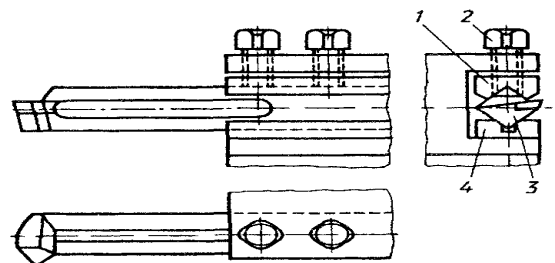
Жорсткий розточувальний різець В. К. Семинського: 1 - притискна планка; 2 - болт різцетримача; 3 - різець; 4 - підкладка-призма
